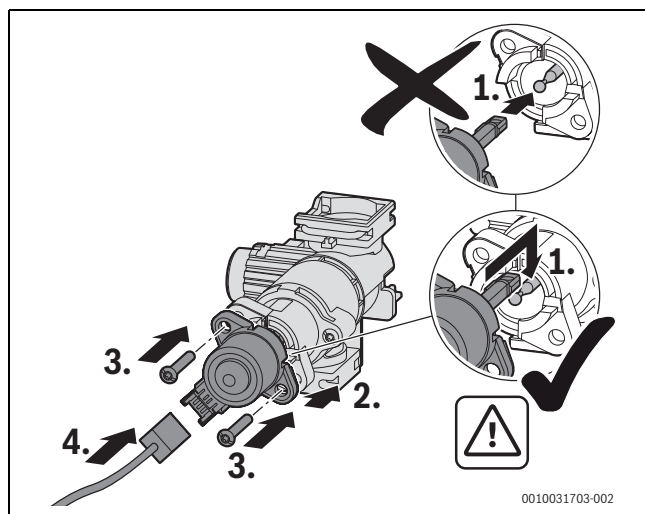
Instalar el motor en la válvula de 3 vías (variante con tornillos)
